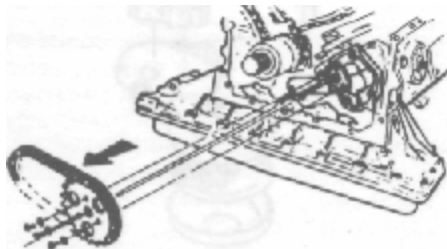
Снятие звездочки и цепи масляного насоса - Двигатель В280F
